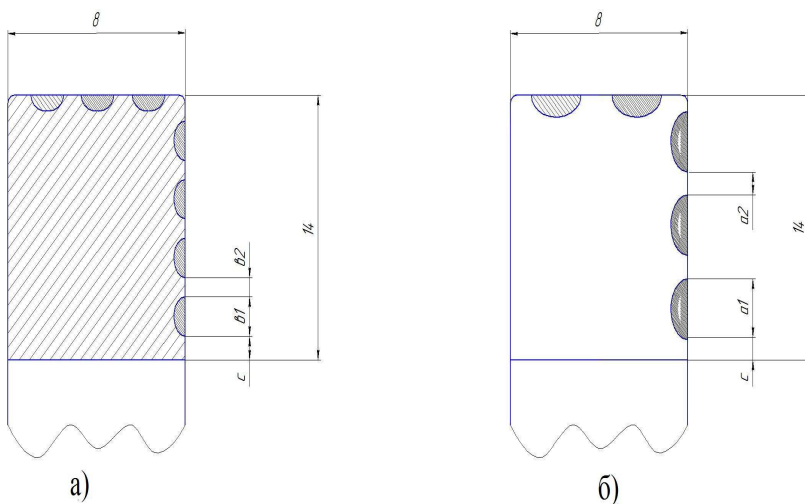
Расположение лазерных дорожек на рабочей поверхности поршневых колец (СДВС 6 ЧРН 36/45):
